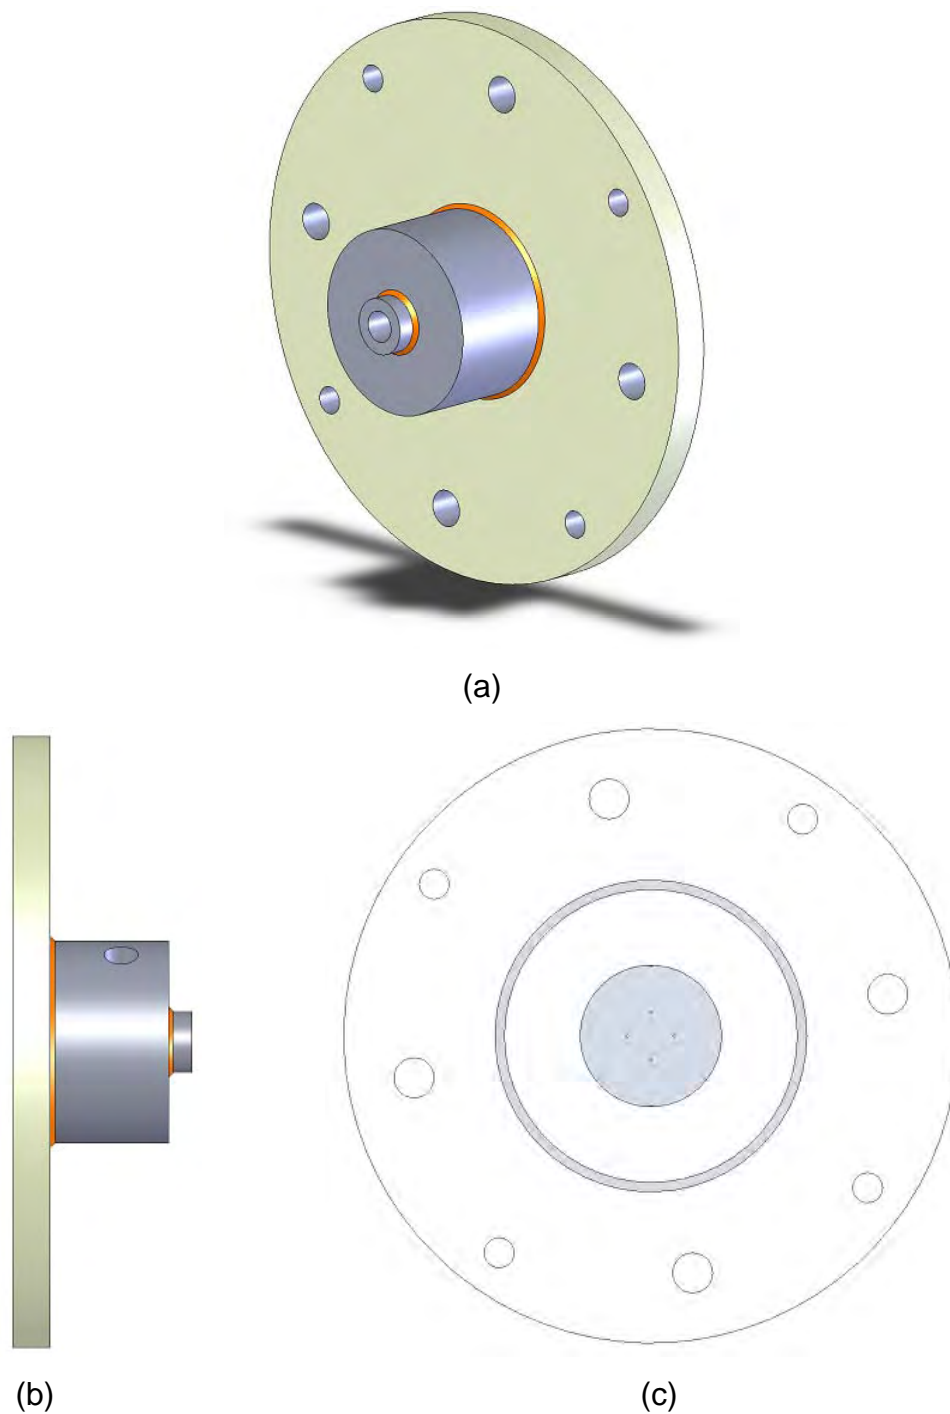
Injetor bipropelente fabricado em aço inox 316. (a) Perspectiva isométrica, (b) Vista Lateral, (c) Vista Frontal.
